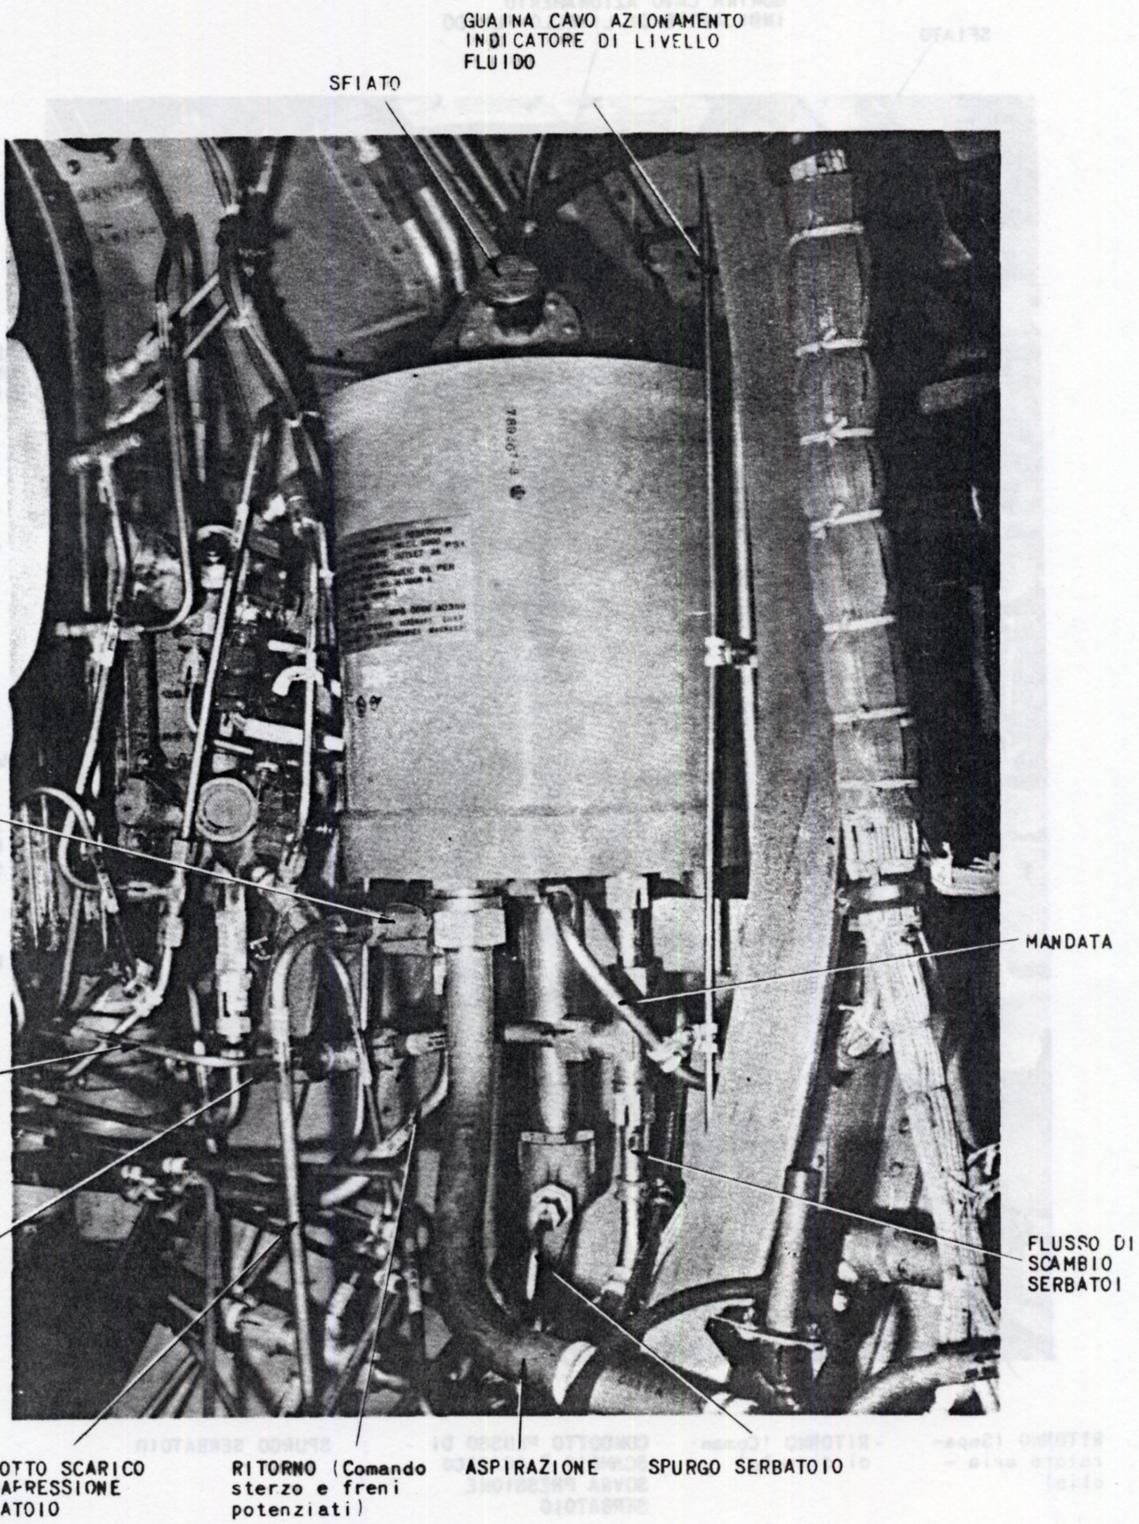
Installazione serbatoio impianto idraulico N. 2.
